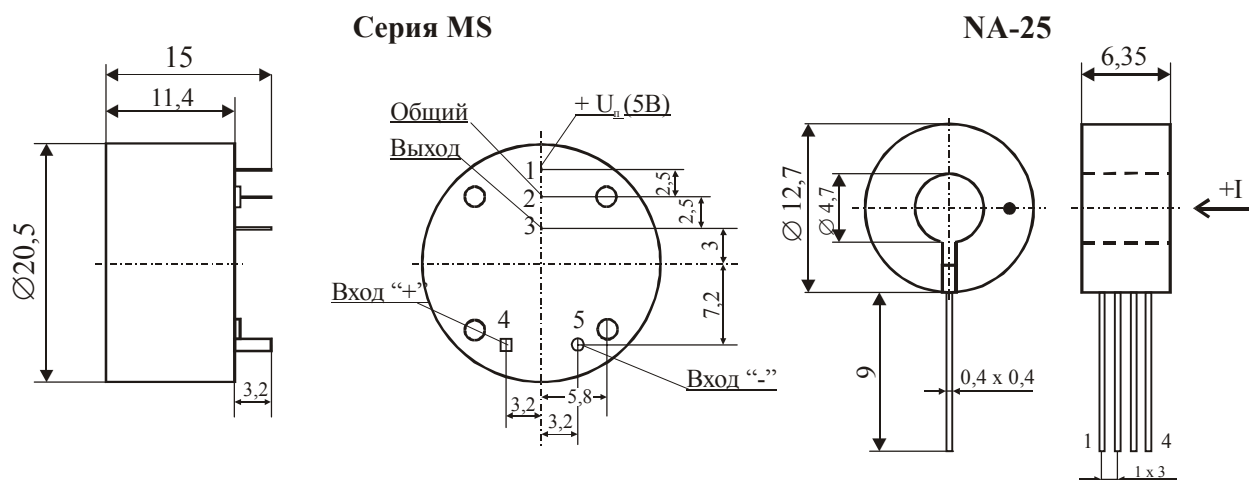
Внешний вид и габаритные размеры датчиков тока типа MS
